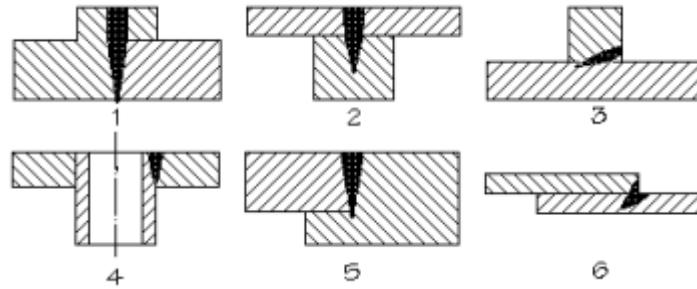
Soldagem em locais de difícil acesso ou inacessíveis.
